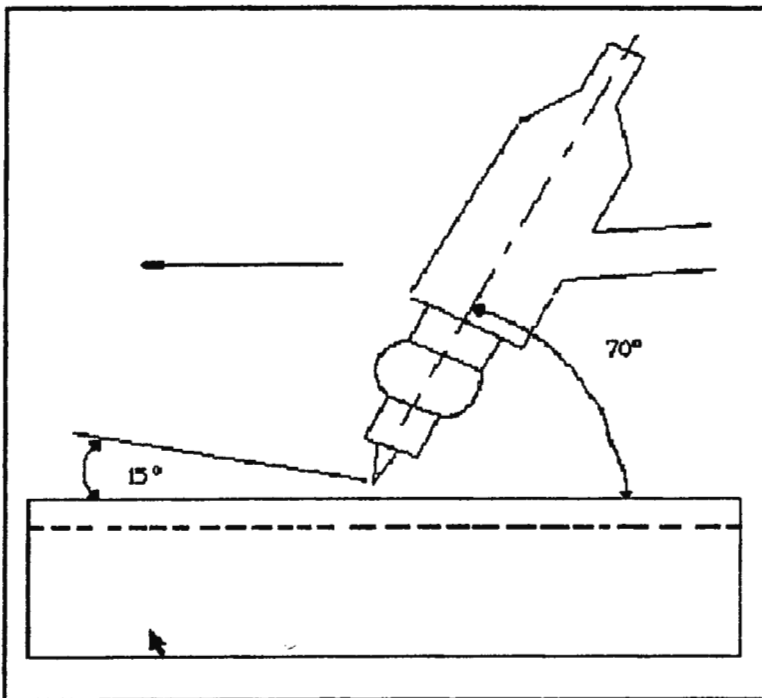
Posición de la pistola y el metal de aporte en relación a las piezas a soldar vista de frente
